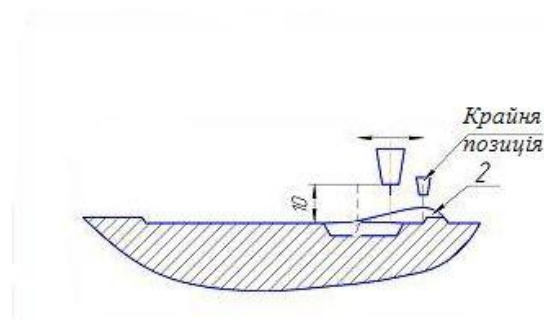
Схема підготовки зварювального пальника до накладення другого валика
